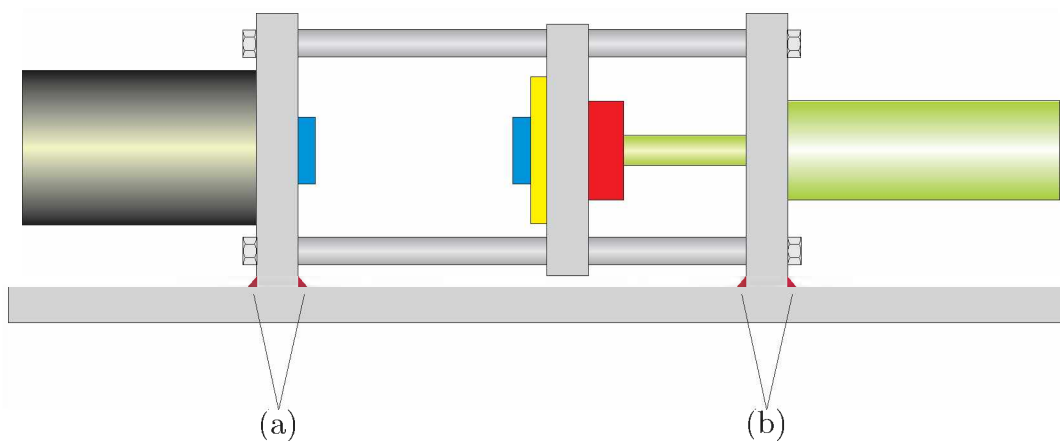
Anbindung der Führungsvorrichtung an die Bodenplatte durch eine Schweißkonstruktion: Durch die Anordnung einer durchgehenden Schweißnaht an den Punkten (a) und (b) ist die Anbindung an die Bodenplatte zu bewerkstelligen.
